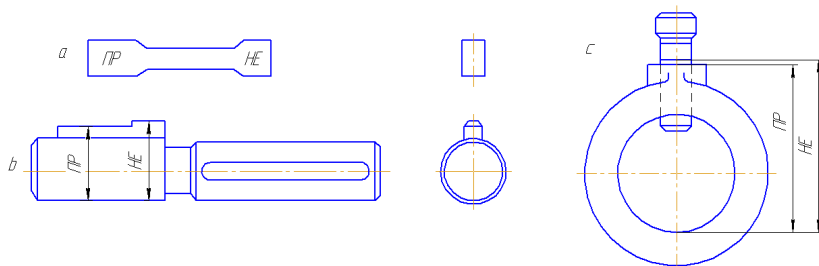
Калибры для контроля деталей шпоночных соединений:
